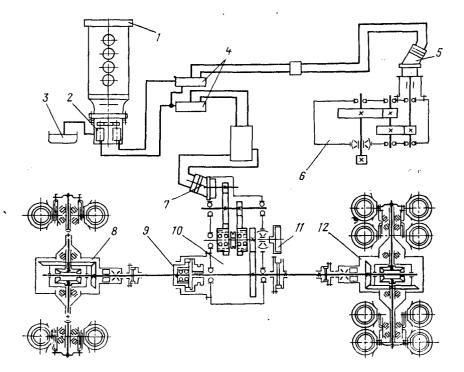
Гидрокинематическая схема привода хода и поворота экскаватора ЭО-3322
